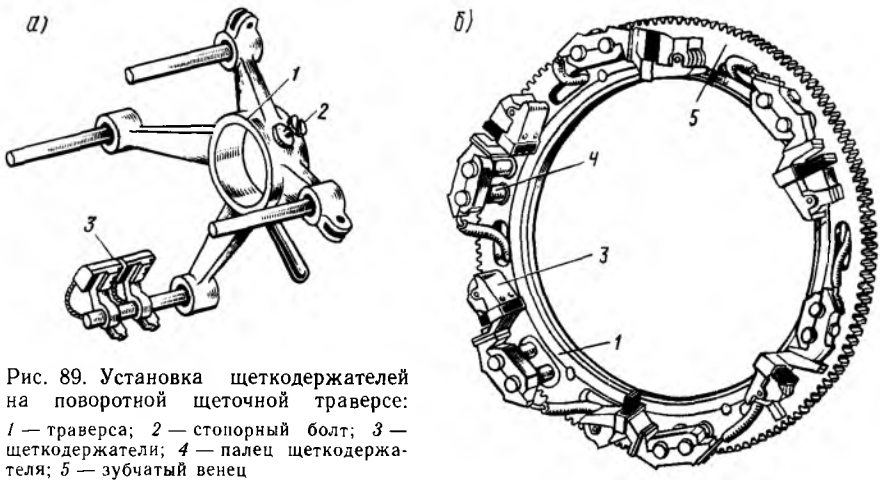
Установка щеткодержателей на поворотной щеточной траверсе: 1 — траверса; 2 — стопорный болт; 3 — щеткодержатели; 4 — палец щеткодержателя; 5 — зубчатый венец
